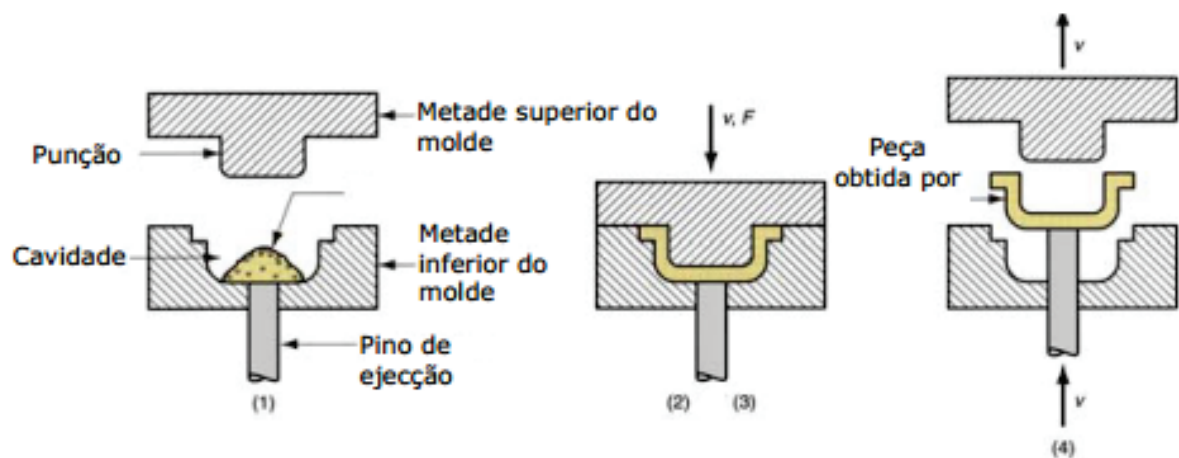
Esquema de moldação por compressão (Universidade Técnica de Lisboa).
